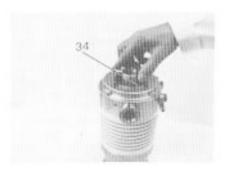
Einstellring 34 herausschrauben Unscrew setting ring 34 Dévisser la bague de réglage 34
